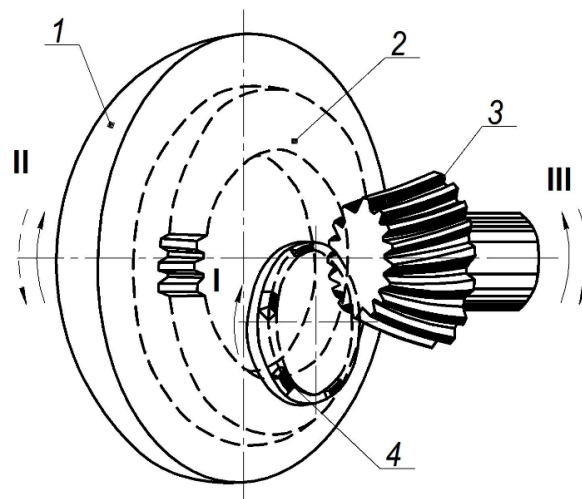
Схема нарізування конічних коліс із круговими зубами торцевими зуборізними головками:
